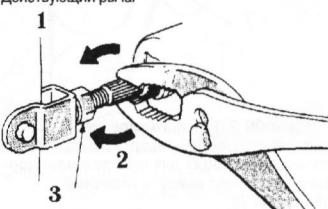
б Используйте плоскогубцы для поворачивания действующего рычага усилителя тормозов, чтобы отрегулировать высоту и свободный ход педали тормоза
